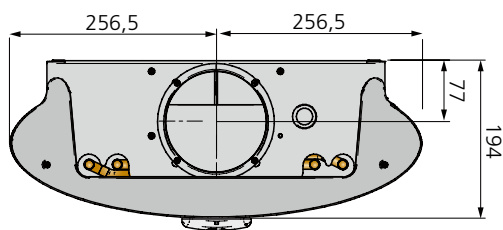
Dimensions ADRIATIC AWC Ellips, vue arrière du raccordement aéraulique
